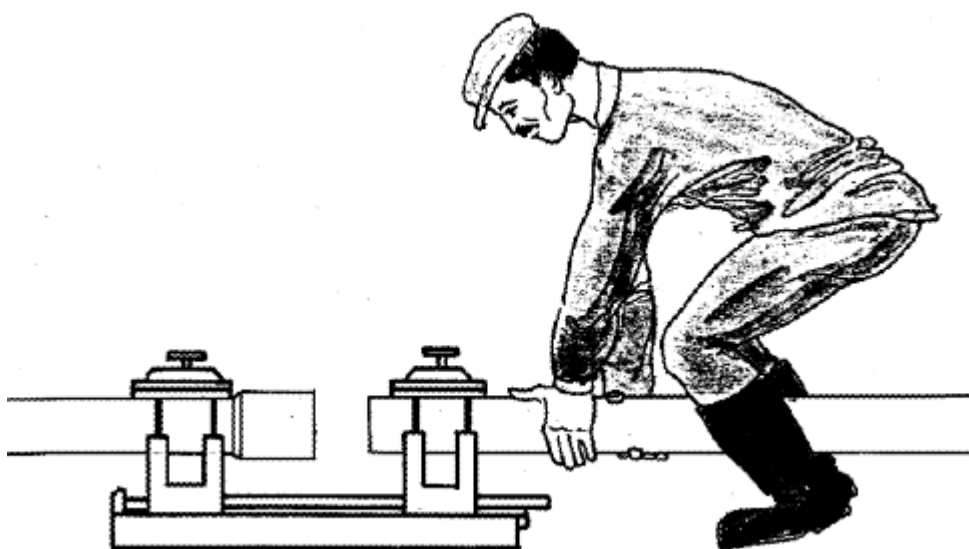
Подготовка зажимного приспособления к работе и крепление.
